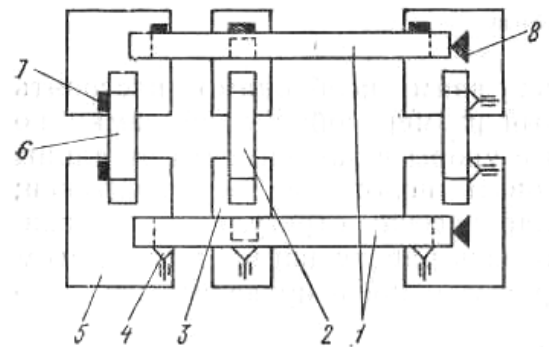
Схема раскладки заготовок в вайме ВГС при сборке изделия с импостом:
